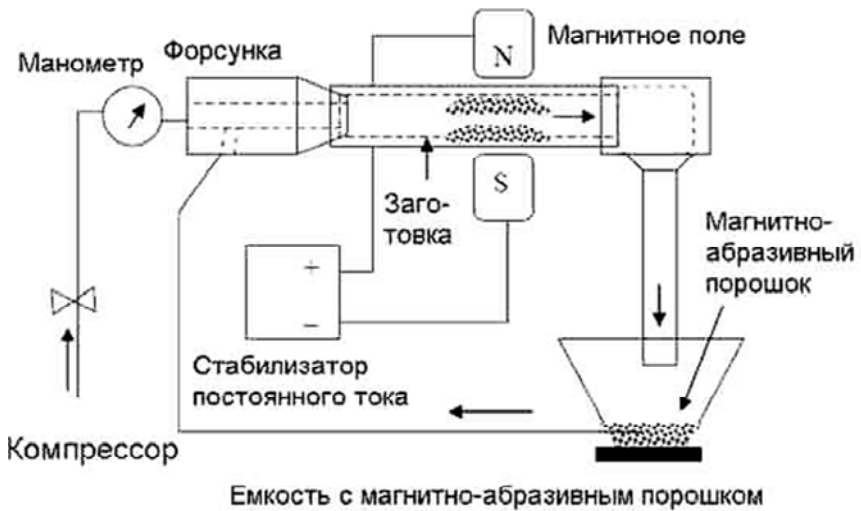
Блок-схема обработки внутренней поверхности полой цилиндрической заготовки магнитно-абразивной струей
